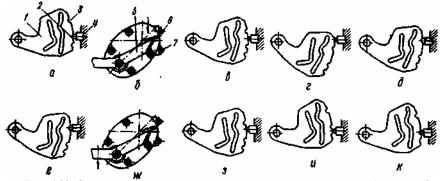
Схема регулировки механизма ножного переключения: ( - сектор; 2 - фиксирующая лунка 2-й передачи; 3 - фиксирующая лунка 3-й передачи; 4 - фиксатор; 5 - педаль; 6 - верхний упор - регулировочный винт; 7 - нижний упор - регулировочный винт
